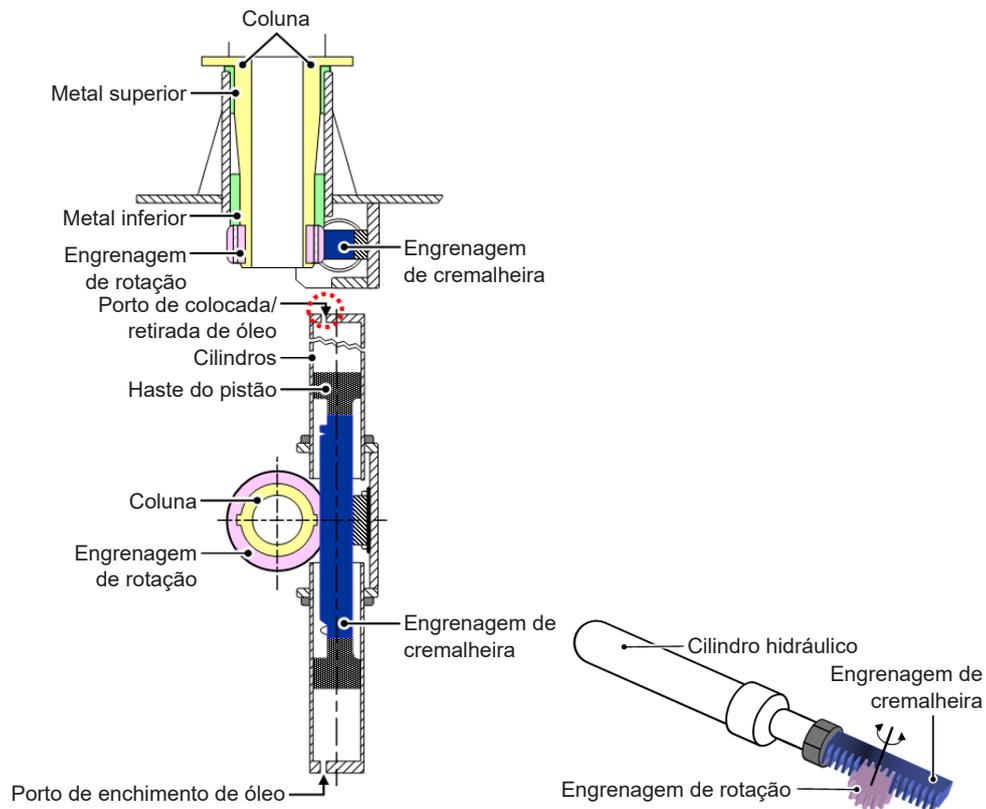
Mecanismo de giro da grua carregadora de caminhões (tipo de engrenagem de cremalheira)
